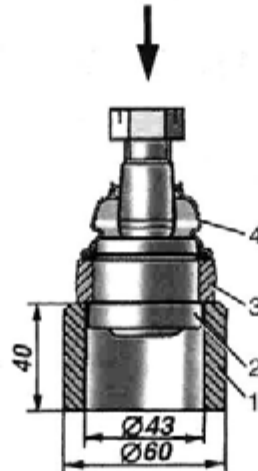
Выпрессовка шарнира рулевых тяг:
